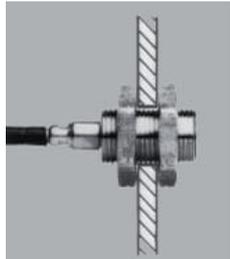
Geschirmter Sensor mit Gewinde in Standardmontage
